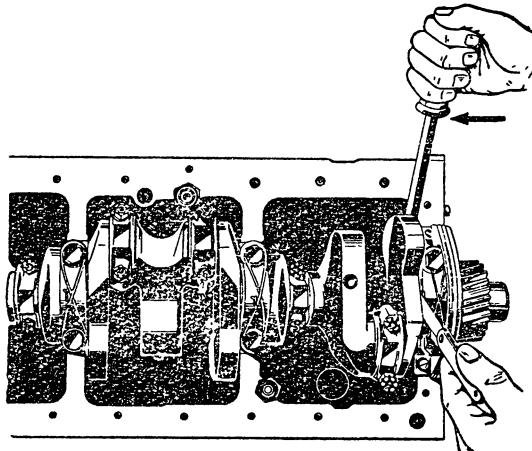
Проверка зазора между задней упорной шайбой и буртиком переднего коренного подшипника
